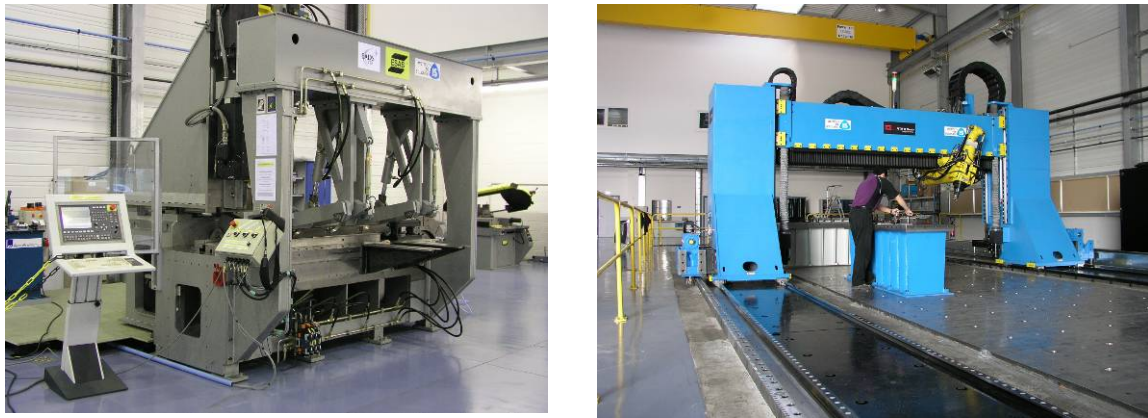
Equipement de soudage FSW de l'Institut de Soudure (Metz)
